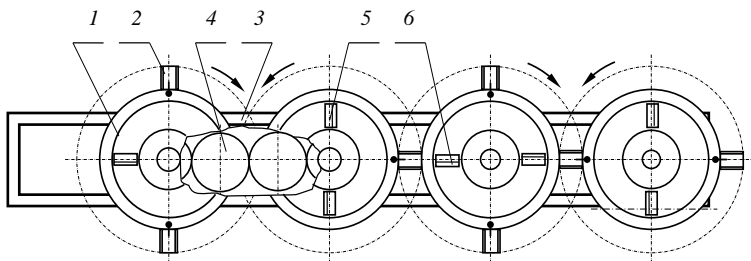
Режущий аппарат с роторами, имеющими радиальные прорези с отогнутым краем: 1 – ротор; 2 – ножи; 3 – корпус; 4 – приводные шестерни; 5 и 6 – радиальные прорези с отогнутым краем
